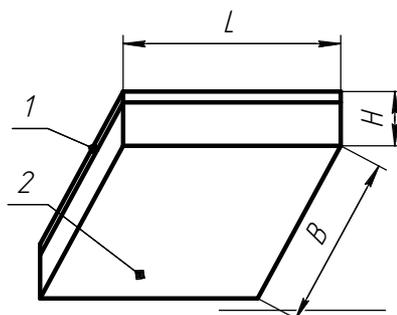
ДПО46-48; 1. Корпус в сборе, 2. Рассеиватель
